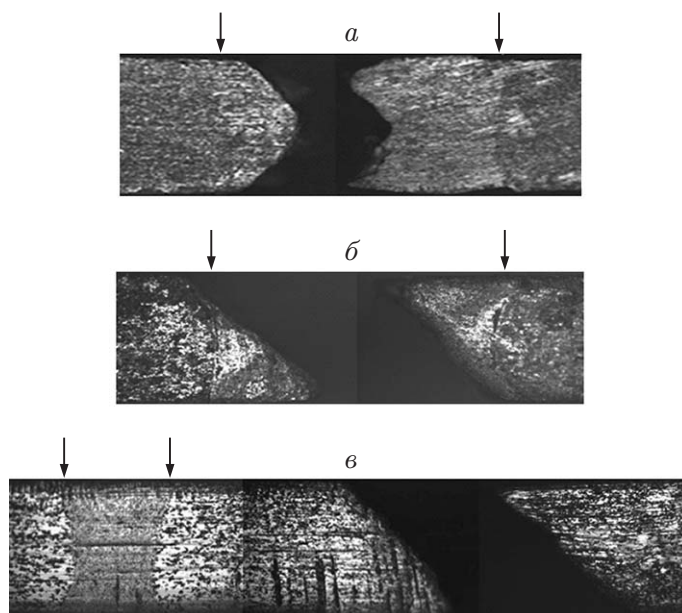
Макроструктура сварных соединений образцов ($\times 5$):
